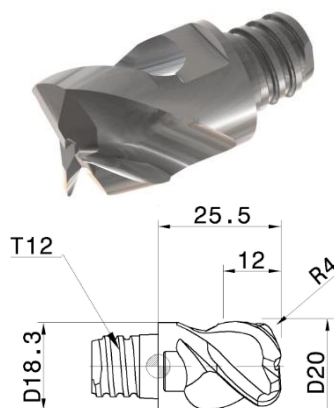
Фрезерна головка MM EA200B12R4.0-3T12
